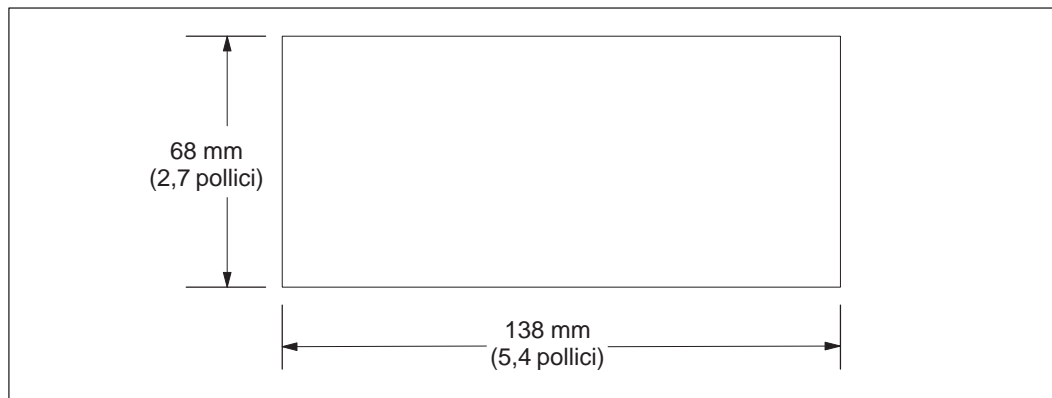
Dimensioni del foro nella superficie di montaggio
